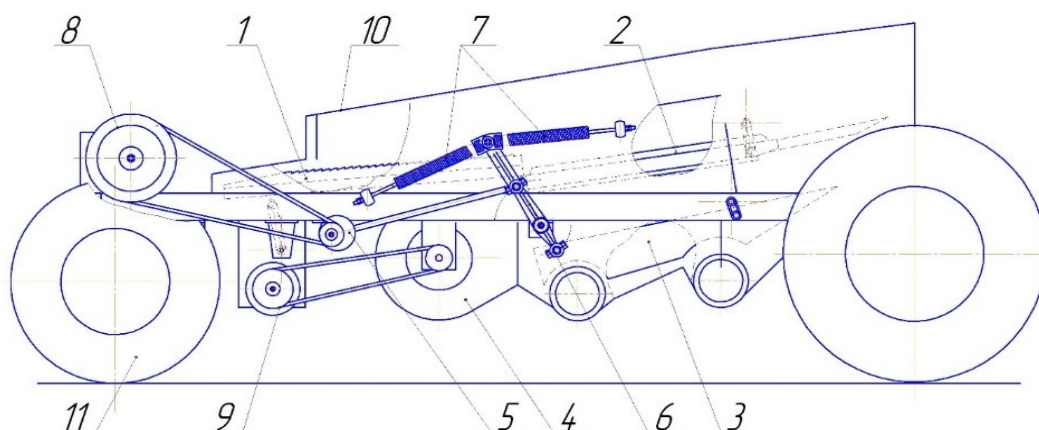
Схема экспериментальной установки: 1 – транспортная доска; 2 – верхнее решето; 3 – нижнее решето; 4 – вентилятор очистки; 5 – кривошипно-шатунный механизм; 6 – двуплечий рычаг; 7 – пружинные аккумуляторы; 8 – привод колебательного вала системы очистки; 9 – привод вентилятора системы очистки; 10 – каркас; 11 – упругие опоры.
